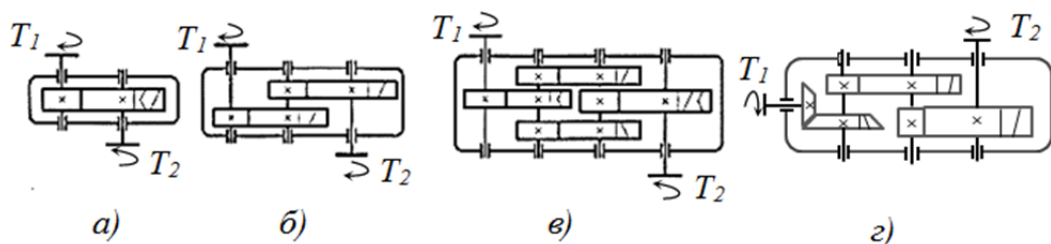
Схеми циліндричного (а,б,в) та комбінованого, конічно-циліндричного (г) редукторів.
